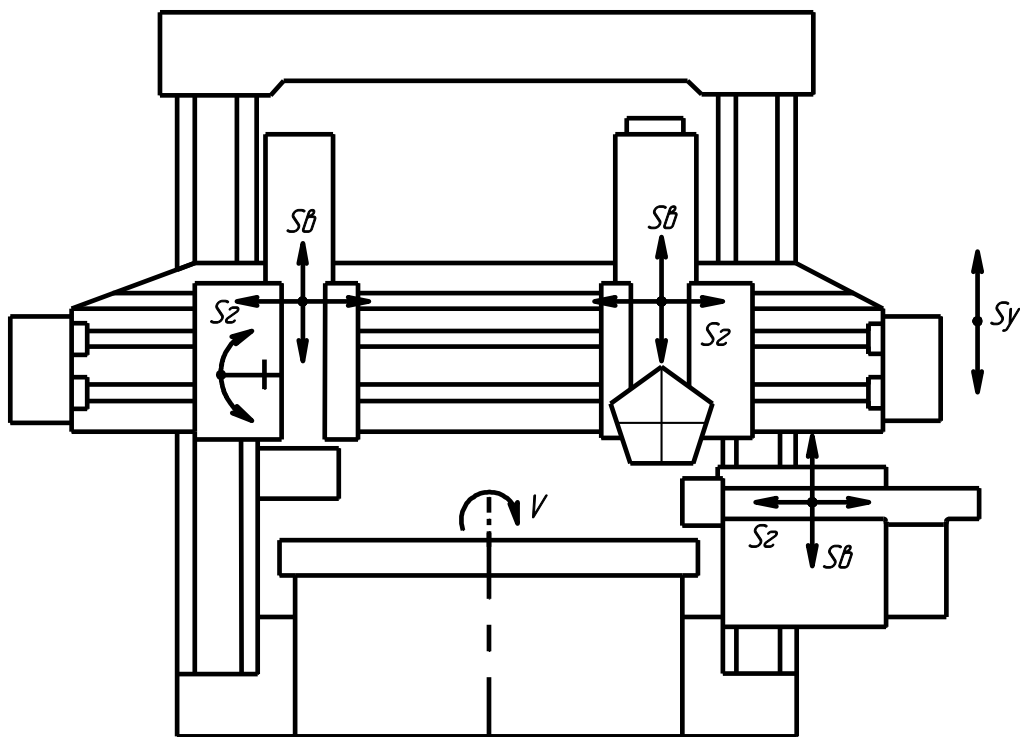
Загальний вигляд токарно-карусельного верстата
